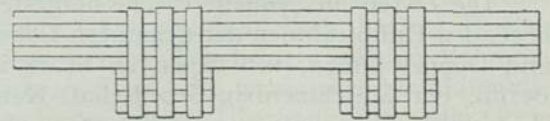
Schweißpaket für Kurbelachse.
